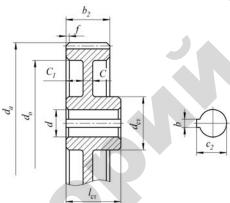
Пример простановки размеров зубчатого цилиндрического колеса
